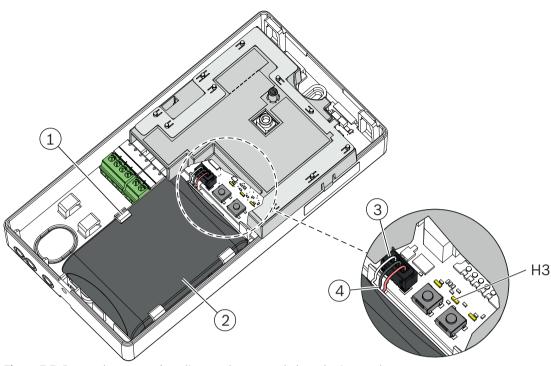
Puerta de acceso vía radio con el paquete de baterías insertado
